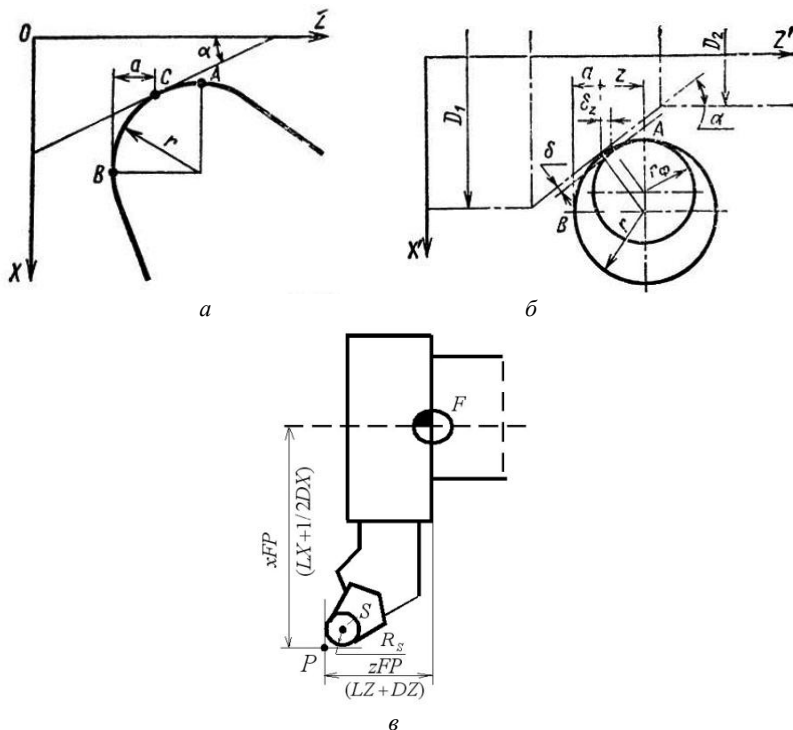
Зміщення розрахункових точок різання при обробці різних поверхонь різцем із закругленою вершиною (а), похибки обробки при неточному визначення радіуса при вершині (б)[1], та параметри корекції на інструмент при обробці на верстатах з ЧПК (в) [2]
